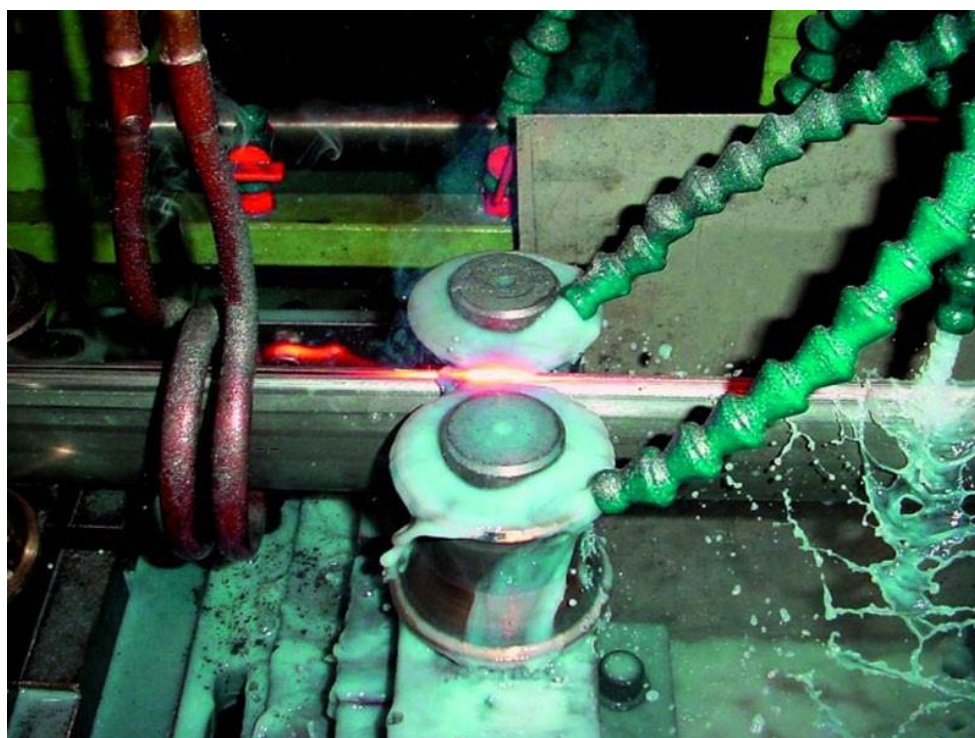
Сварочный индуктор и валки ТЭСА
